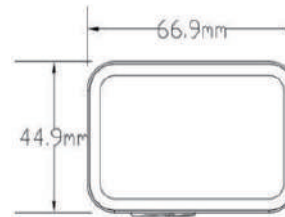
YL61F-F Dessin des dimensions de la vue avant de l'instrument
